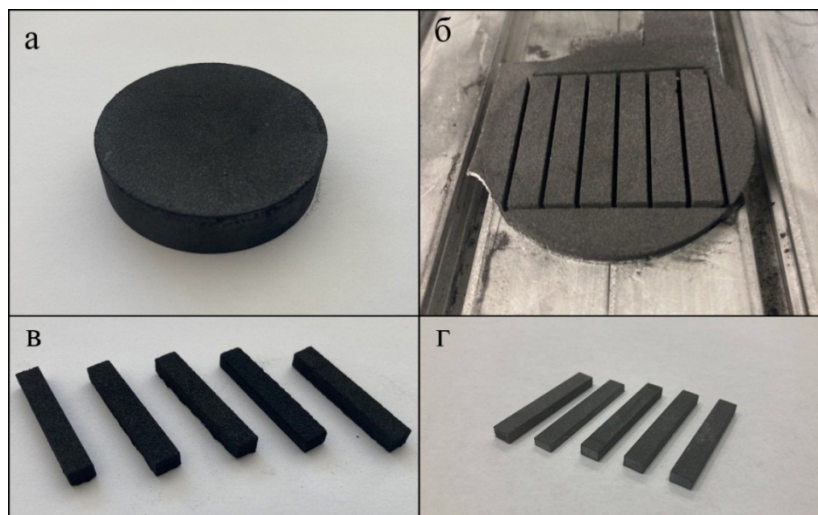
Стадии изготовления образцов (а) –углеродная заготовка с порошком Mo, (б) – заготовка, обработанная на фрезерном станке с числовым программного управлением, (в) – вырезанные образцы перед силицированием, (г) – образцы после силицирования и финишной обработки
